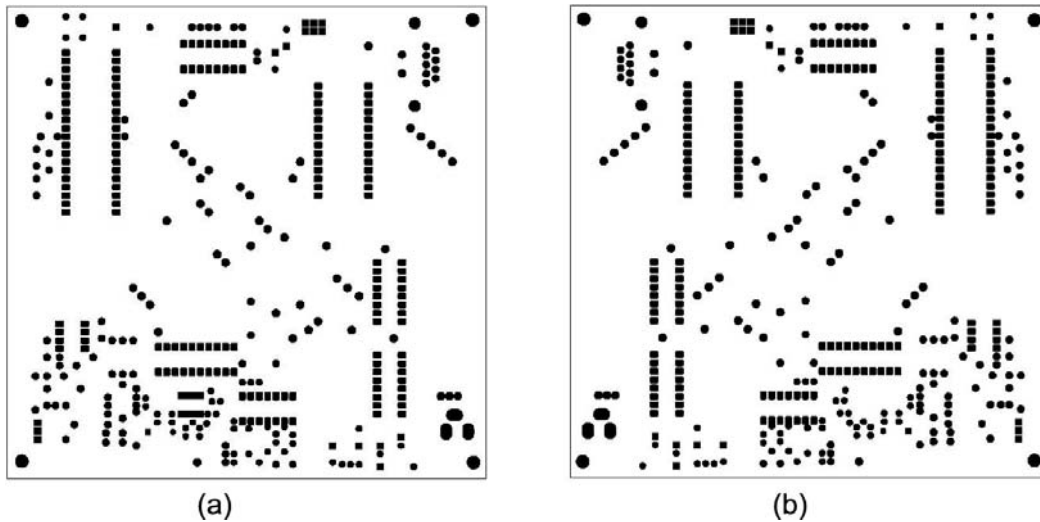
(a) Máscara de ilhas de soldagem da face superior e (b) máscara de ilhas de soldagem da face inferior do circuito.
